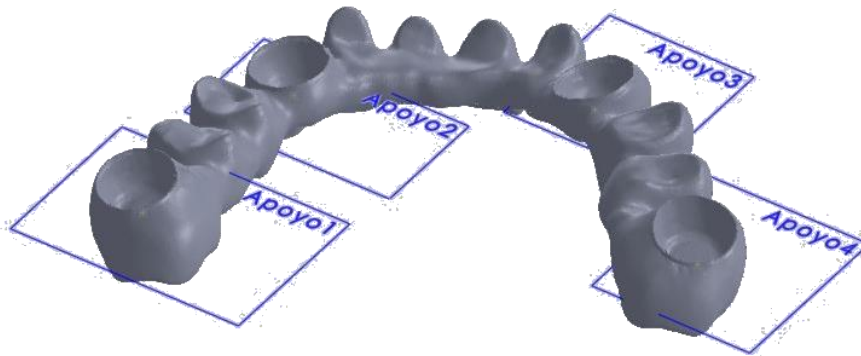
Planos auxiliares para la proyección de los centros de apoyo.
